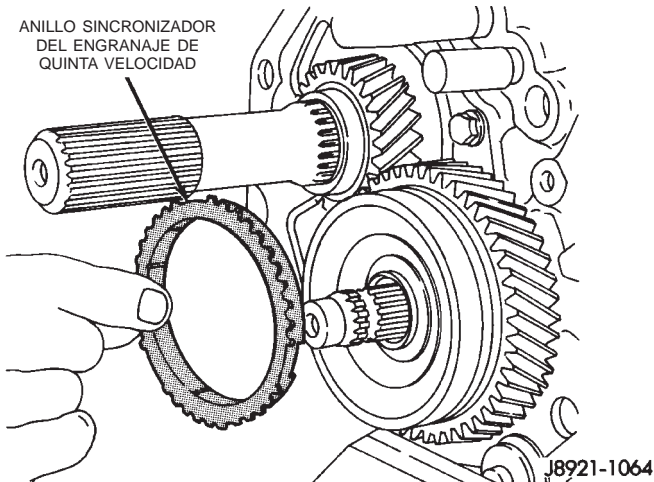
Desmontaje del anillo sincronizador del engranaje de quinta velocidad
